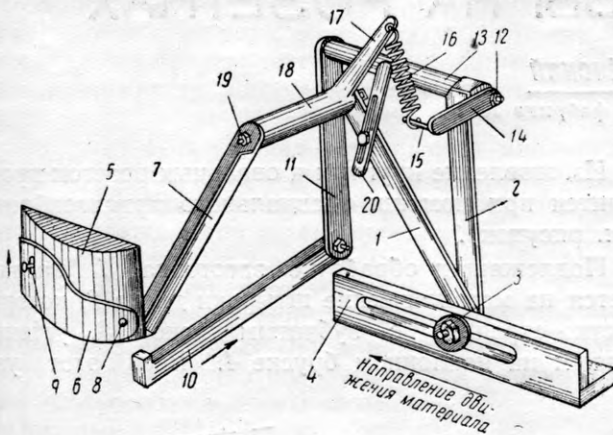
Схема приспособления для ограждения режущей части фрезы
